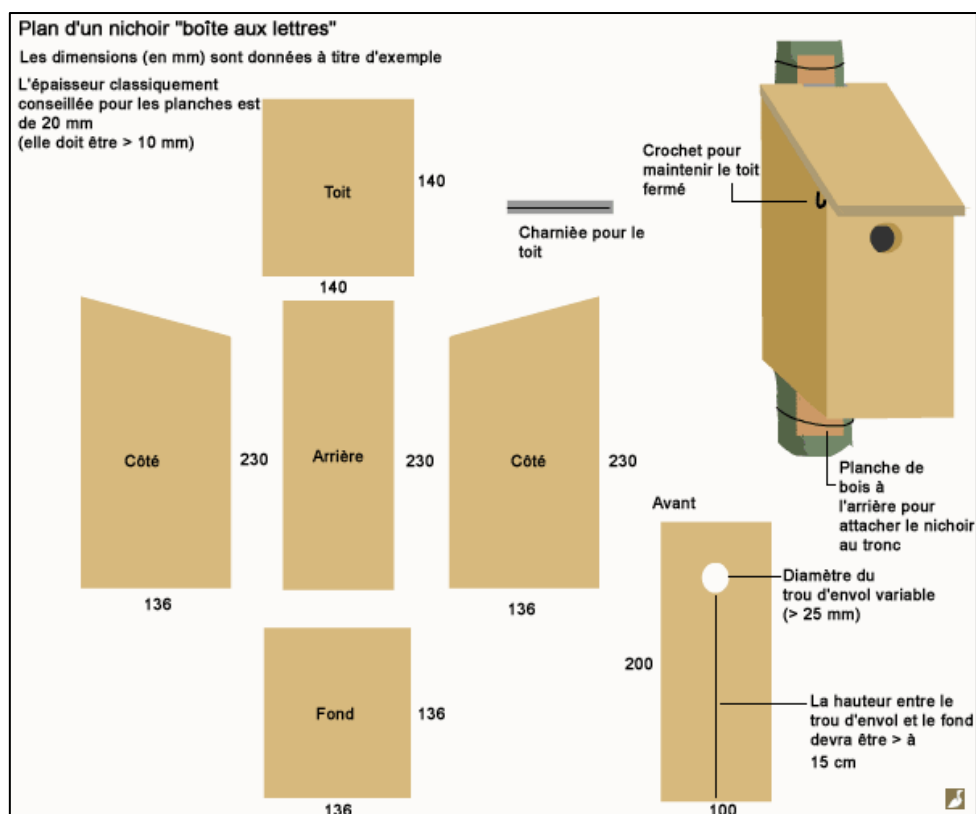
Plan de fabrication d'un nichoir type « boîte aux lettres » permettant d'accueillir des petits passereaux (source : jardiner-autrement.fr).
